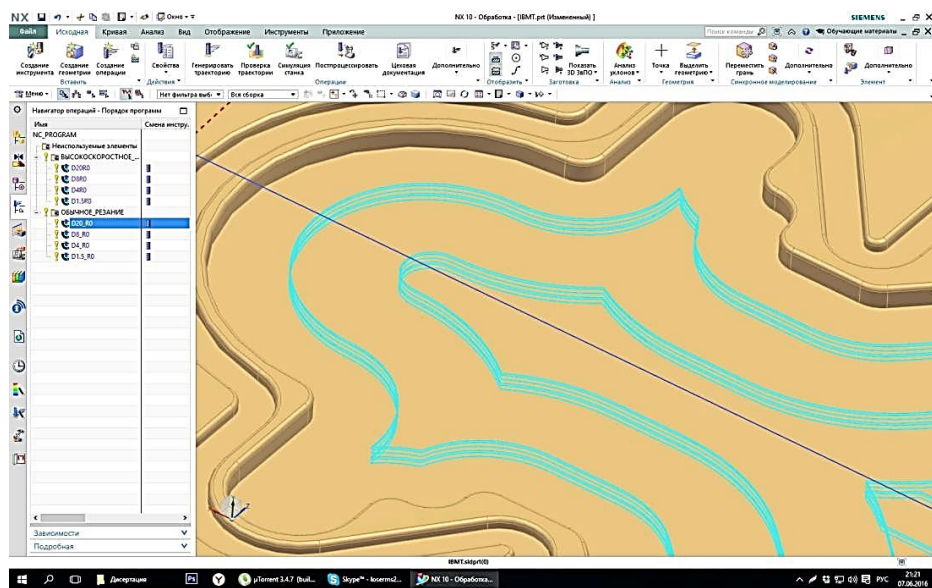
Траєкторія фрези діаметром 20 при звичайному фрезеруванні
